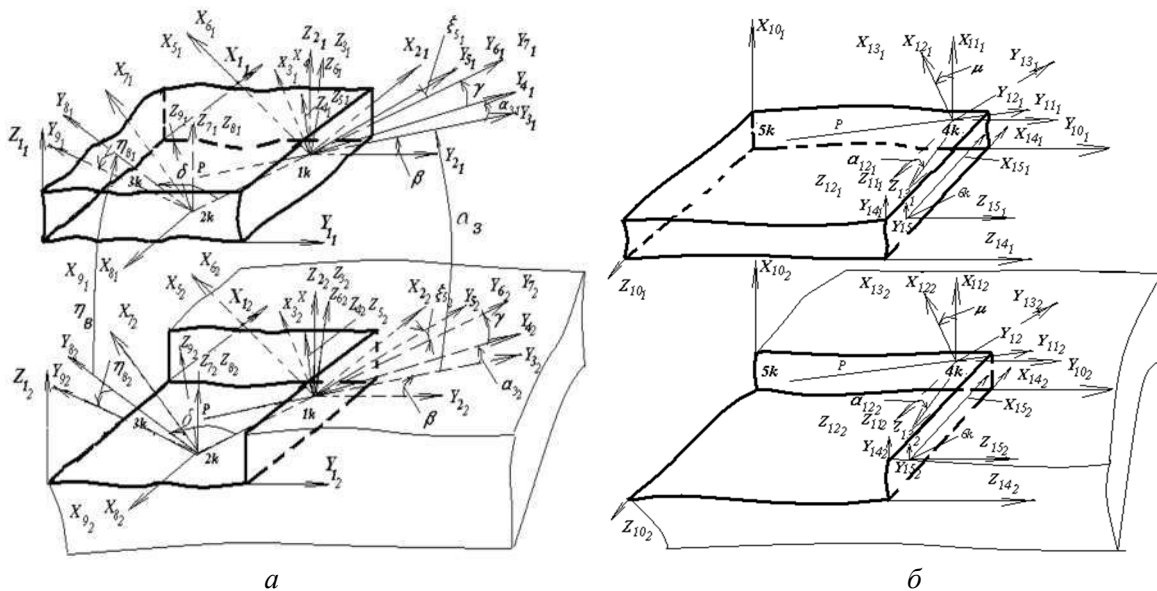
Схема к расчету координат точек контакта СМП и паза корпуса инструмента: а – для опорной поверхности; б – для боковых поверхностей
